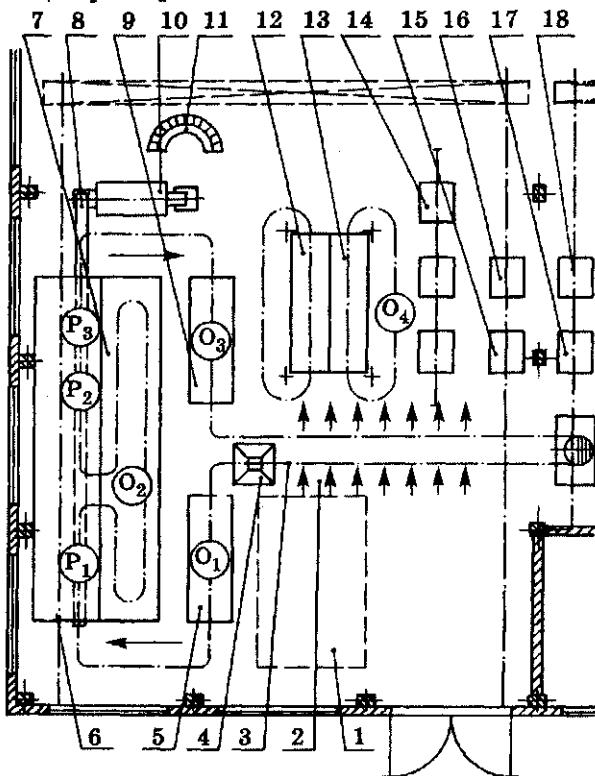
Планировка разборочно-очистного участка двигателей:
